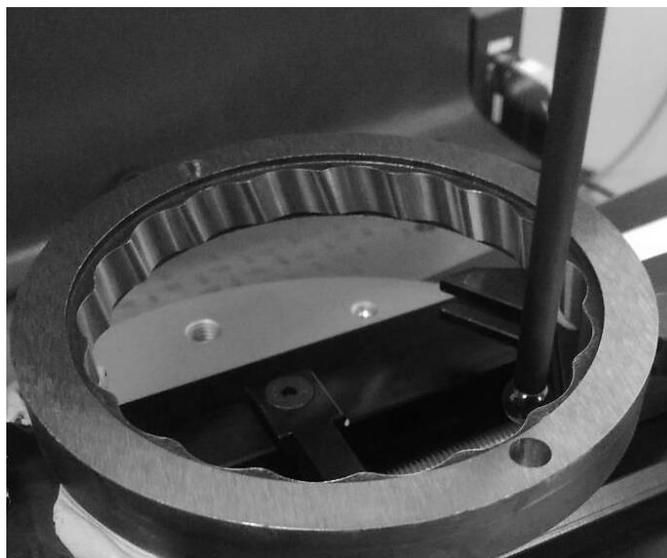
Метрологический контроль точности обработки венца циклоидального редуктора с косозубым зацеплением зубчатых колес
